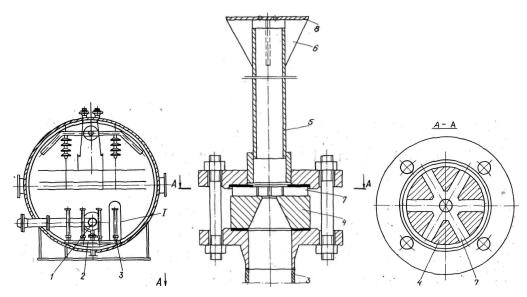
Схема дооборудования горизонтального электродегидратора вертикальными струйными смесителями (1): 1 – продольный коллектор; 2 – поперечный коллектор; 3 – штуцер; 4 – сопло; 5 – смесительный патрубок; 6 – ребро; 7 – паз; 8 – отражатель
